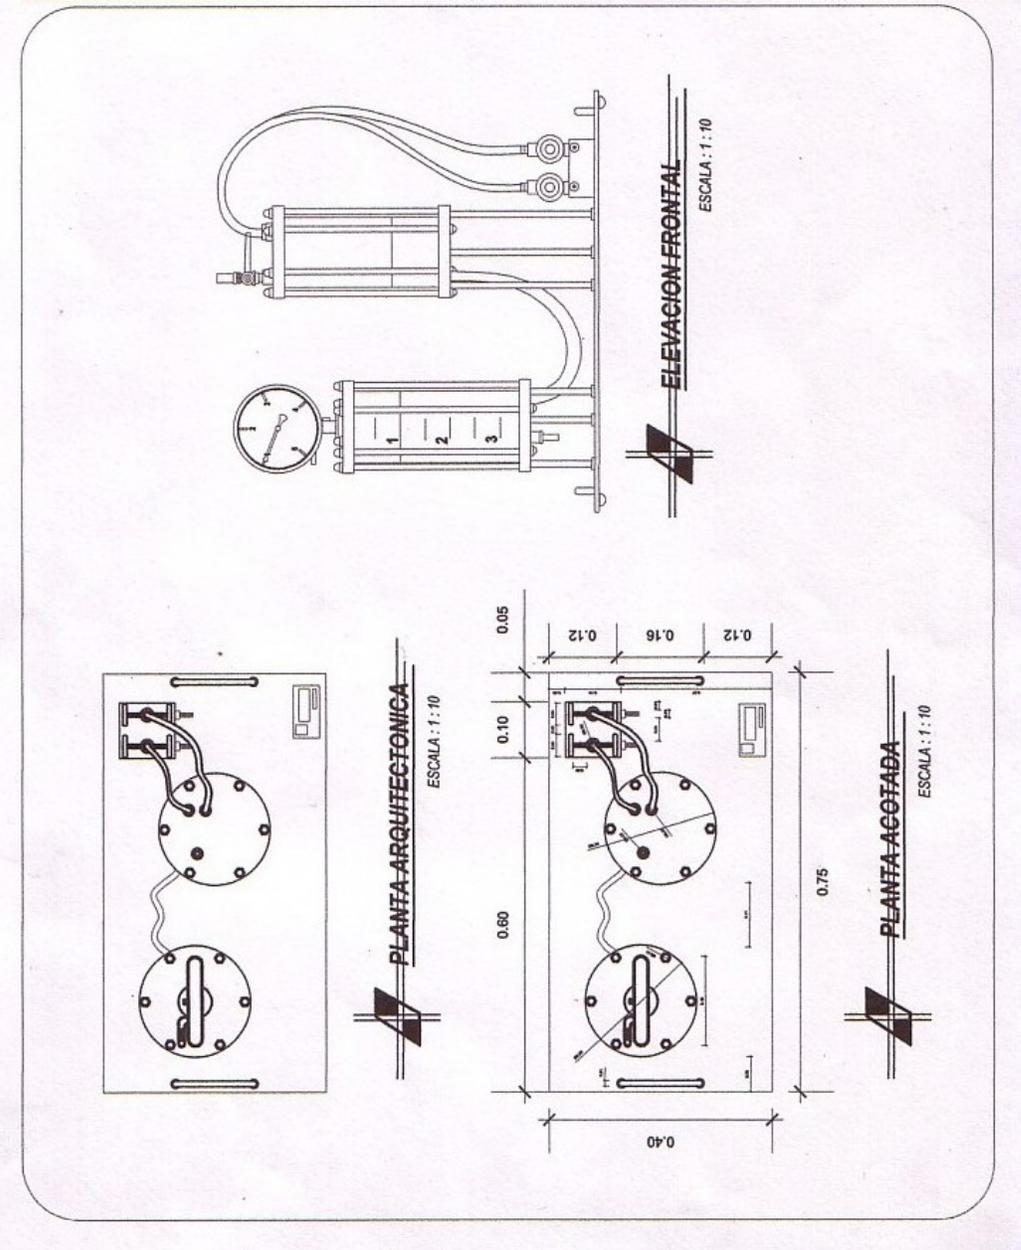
Plano modificado del equipo “Boyle-Méndez Primero”.
